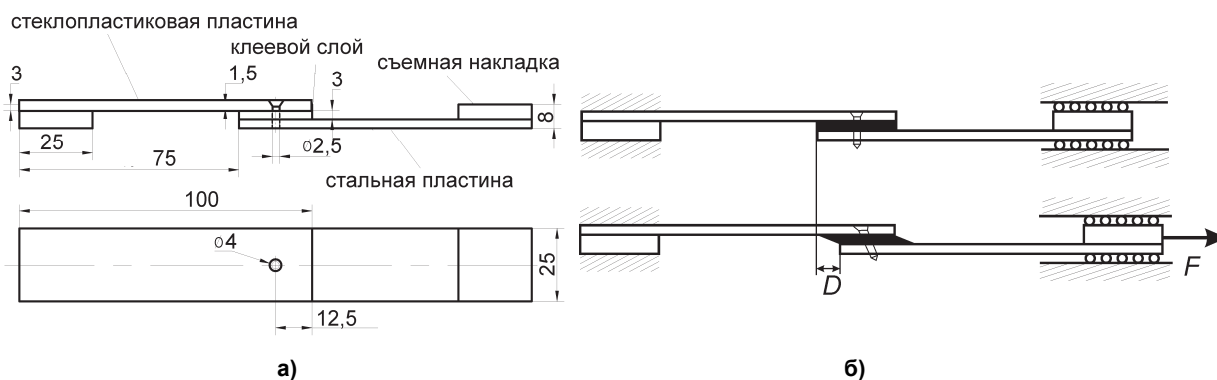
Образец нахлесточного соединения: а – эскиз; б – схема испытаний
